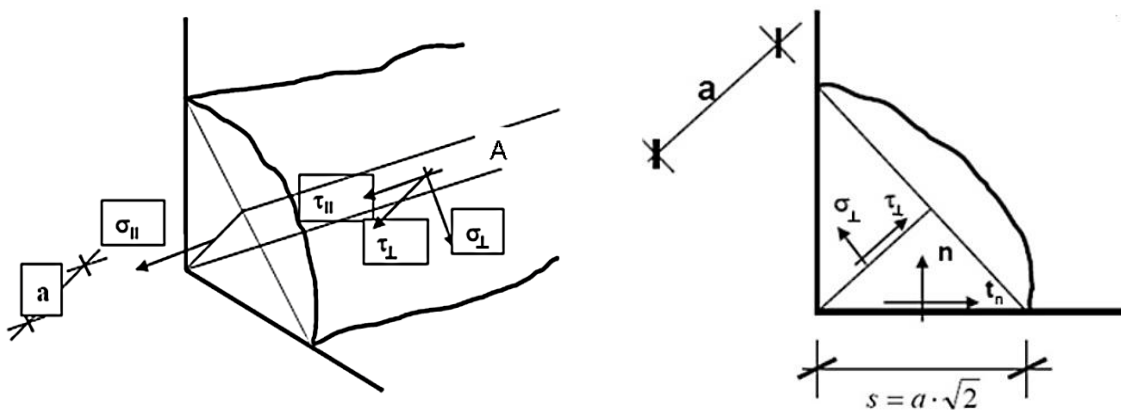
Tensiones en la garganta de un cordón de soldadura.
